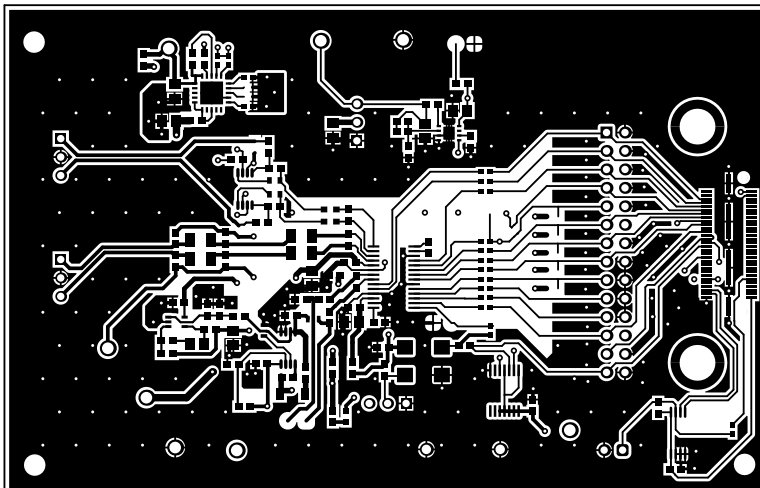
ADS1282EVM 的 PCB 布局 (顶层)
